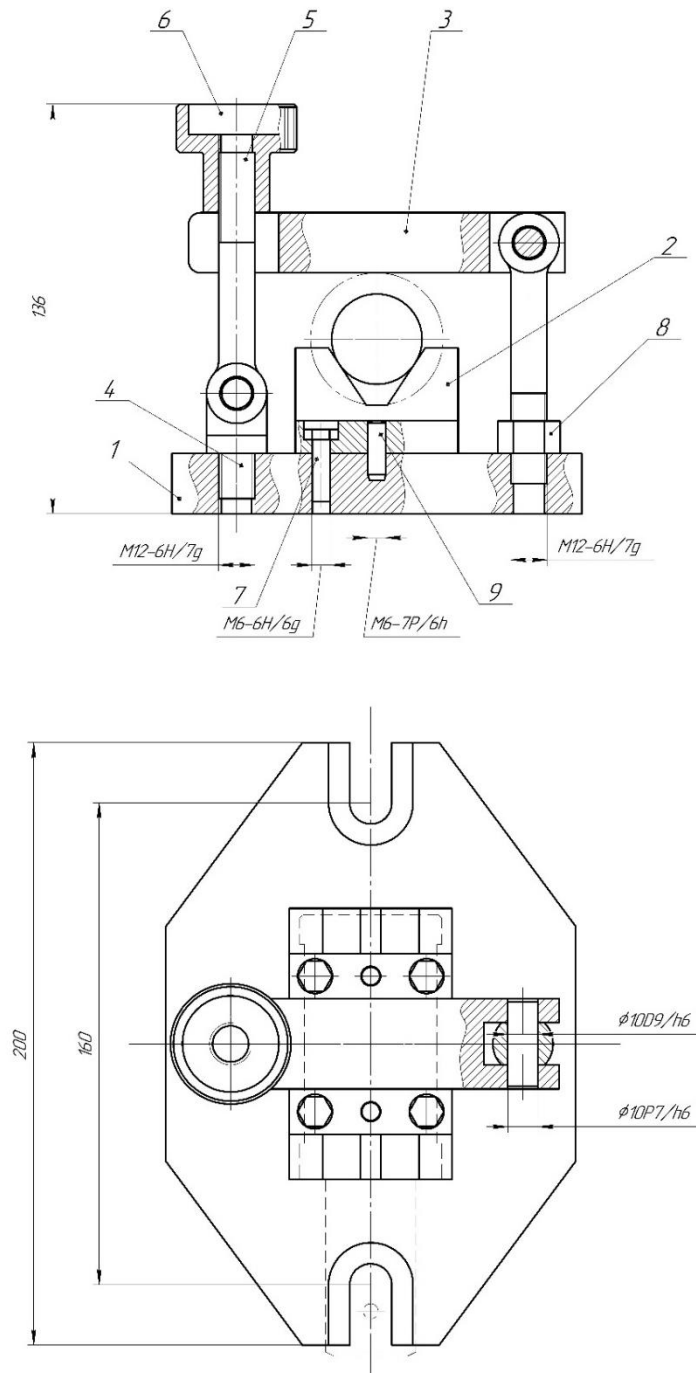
Затискач гвинтовий: 1 – плита; 2 – призма; 3, 4 – стійка; 5 – опора; 6 – гвинт; 7 – втулка; 8 – притискач; 9 – вороток; 10 – гвинт; 11 – гвини; 12 – контргайка; 13 – штифт; 14 – штифт.
